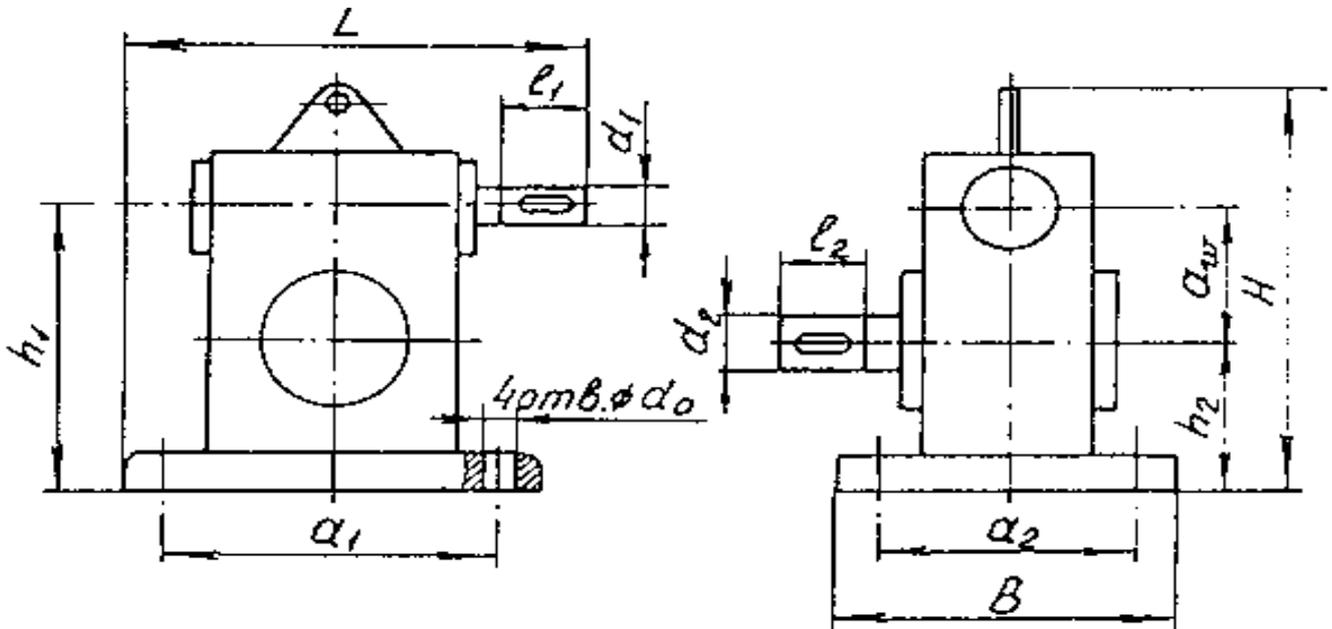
Пример нанесения габаритных и присоединительных размеров редуктора
